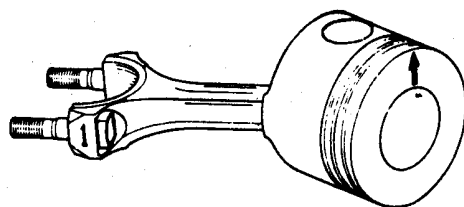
Posiciones relativas de montaje de la biela y el pistón.
